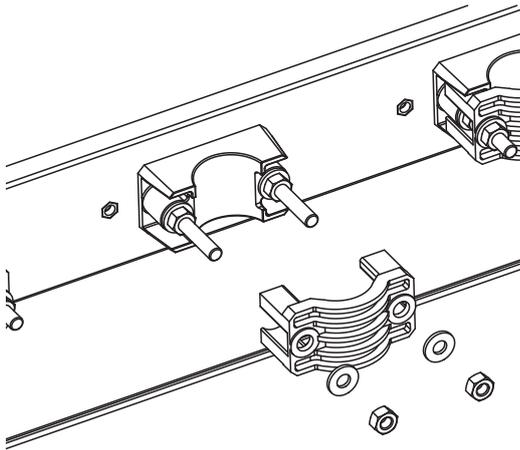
Explosionsdarstellung der Verankerungselemente der Kabel des Schaltfelds RLC
